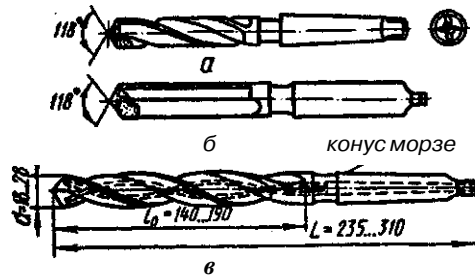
Свердла, оснащені пластинками з твердого сплаву, з гвинтовими (а), прямими (б) канавками і каналами для охолодної рідини (в)
